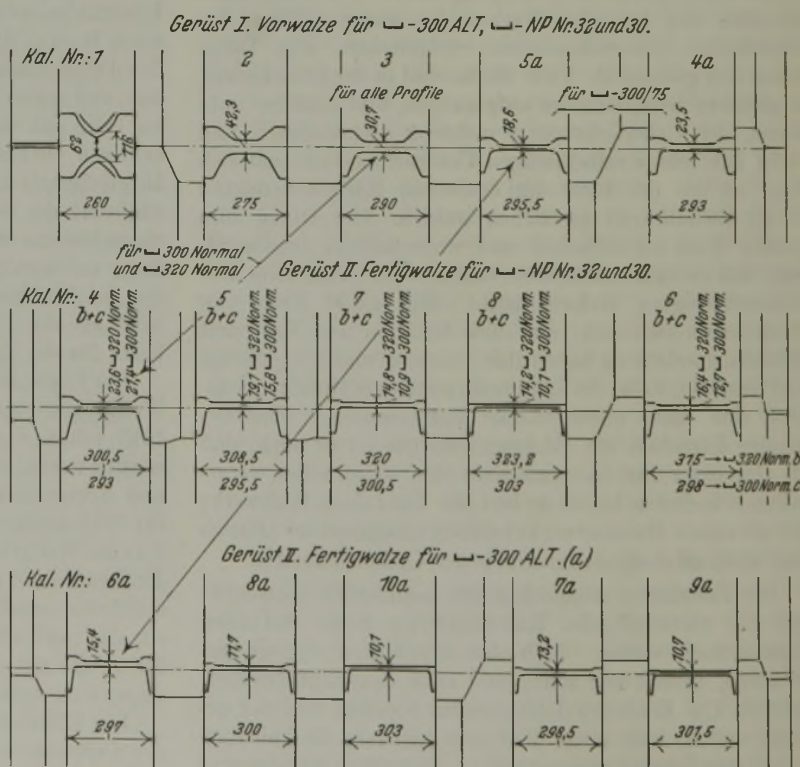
Planung der Walzen für \sqsubset -300 ALT, \sqsubset -NP Nr. 32 und 30. Zweiwalzen-Umkehrstraße, 2 Gerüste. Walzendurchmesser 900 bis 950 mm.
